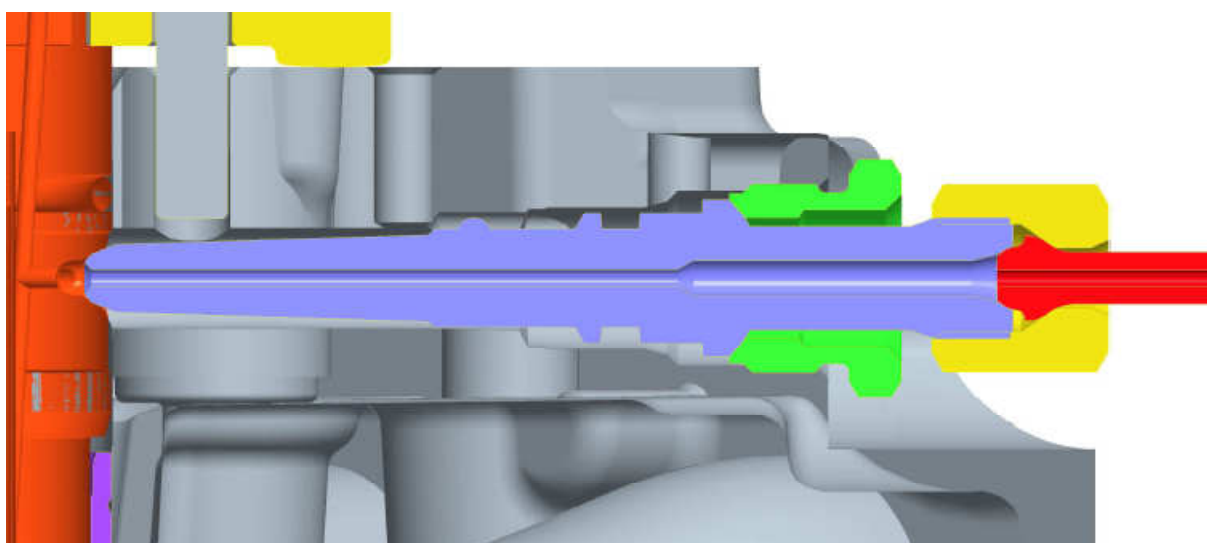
Detailní pohled na vysokotlakou přípojku
